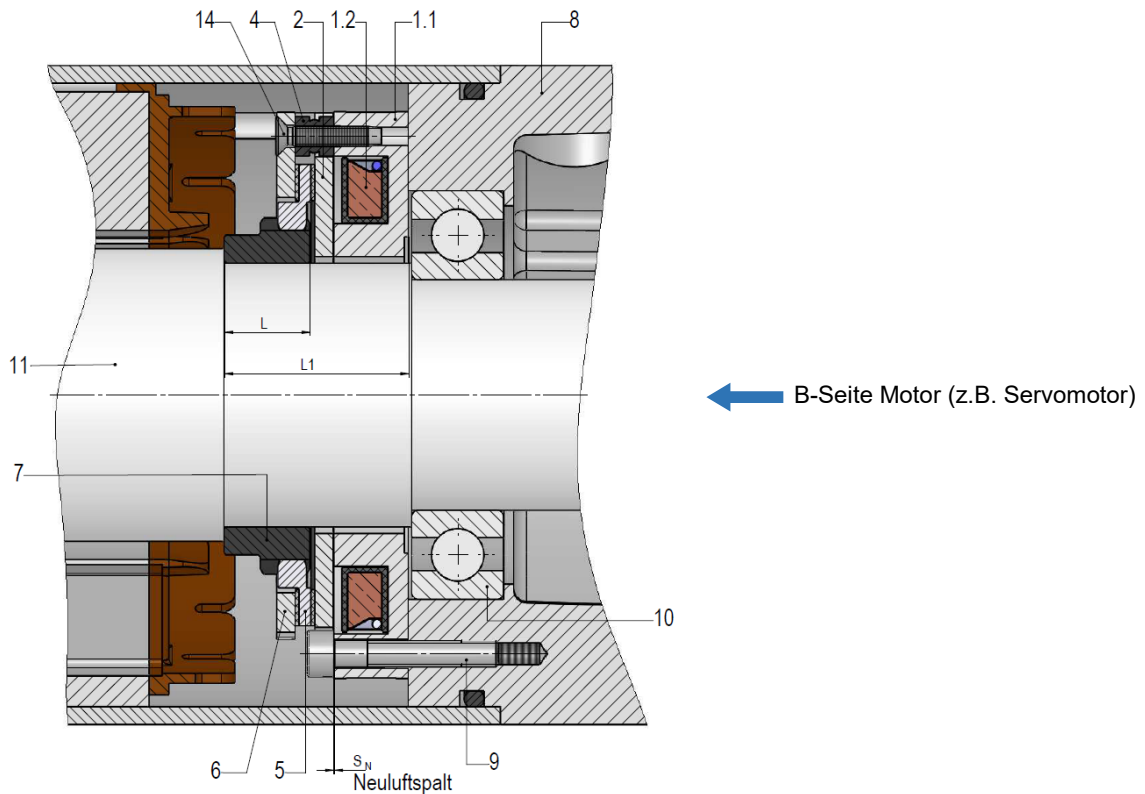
/1: Flanschseitige Befestigung am Beispiel der Federdruck-Einscheibenbremse SL 500..A00 in den Motor (z.B. Servomotor) mit Anschlag des Mitnehmers (7) an der Anschlagshulter der Motorwelle (11) und Verbindung des Mitnehmers (7) mit der Motorwelle (11) durch Presspassverbindung (siehe Kapitel 4.1.2)
